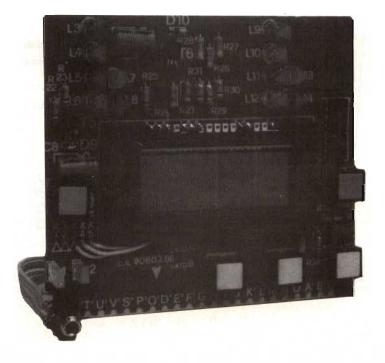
Circuito stampato cod. 90603.67: montaggio dei componenti (lato A).
